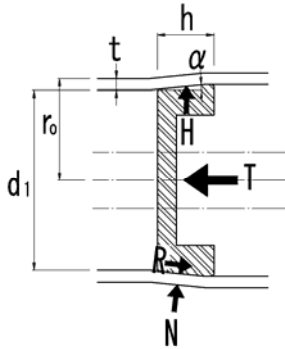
ウェッジプレートの構造寸法 (本論：図-4)
